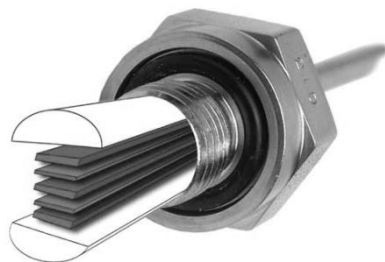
Формування спаю термопар за рахунок зварювання тертям.
